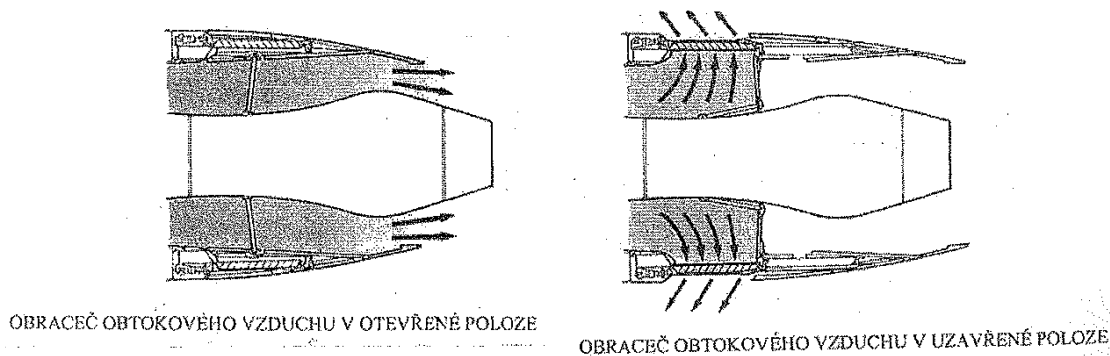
[53] Horní obr. znázorňuje oddělené
